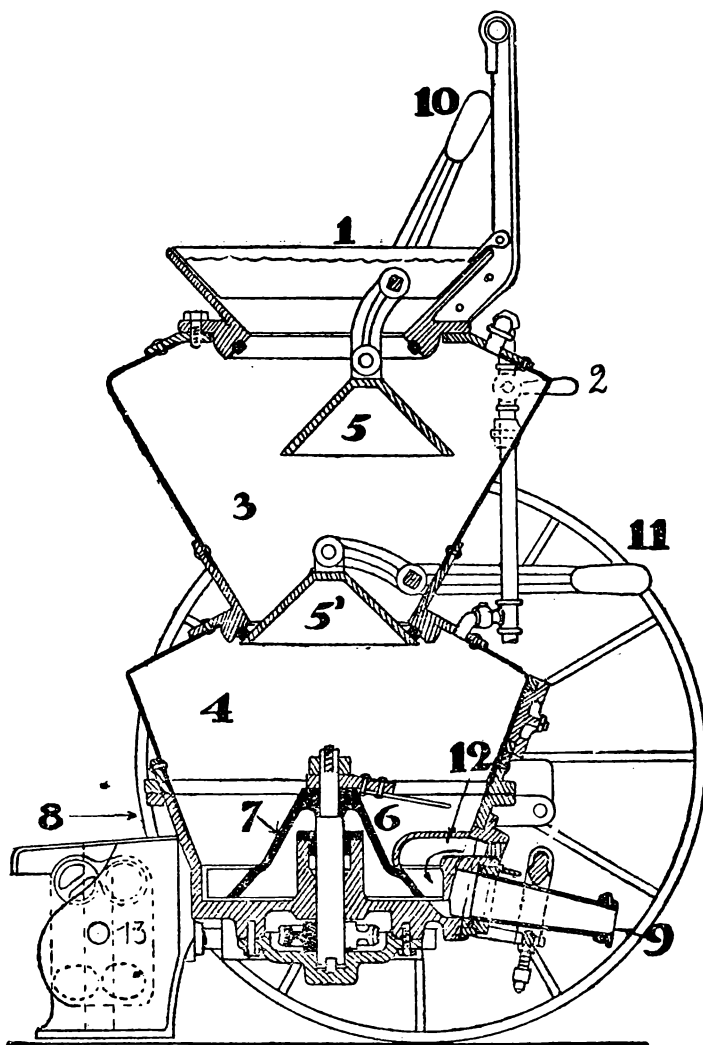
„Цементная пушка“. 1 — загрузочная воронка. 2 — кран на перепуске сжатого воздуха. 3 — верхняя камера. 4 — нижняя камера. 5 — верхний клапан. 5' — нижний клапан. 6 — допалка. 7 — гнездовой ротор. 8 — колесо тележки. 9 — выдувной пистолет. 10 — рукоятка для клапана (5). 11 — рукоятка для клапана (5'). 12 — подача сжатого воздуха для выдувки материала с (7) в (9). 13 — мотор.
